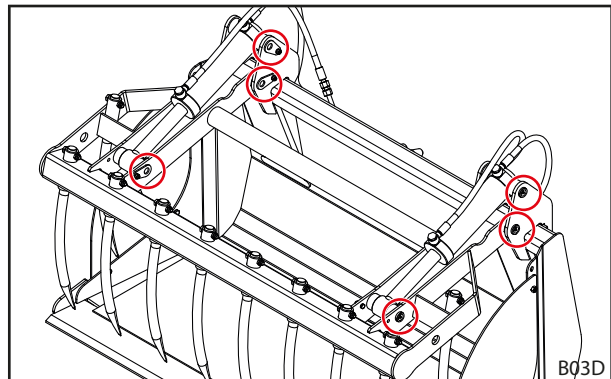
Точки смазки ковша с захватом, двухчелюстной ковш HD и вилы-захват
